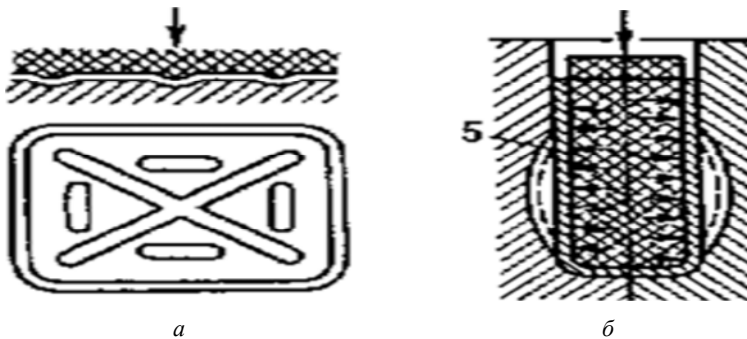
Схема формовки ребер жесткости (а) и формовки с раздачей (б)
